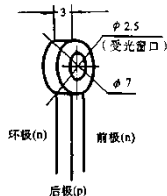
2DUB 型硅光电二极管外形结构尺寸图
